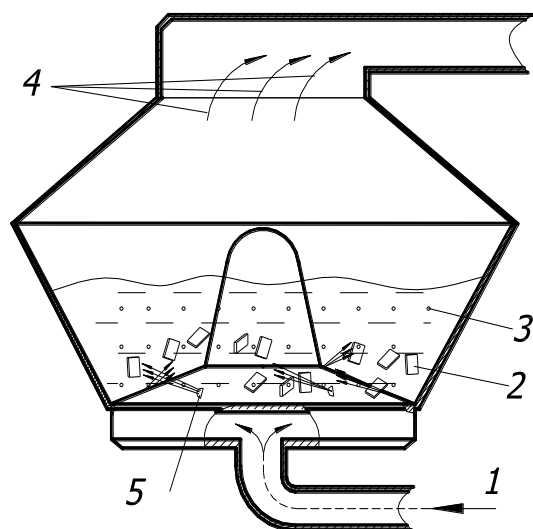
Схема действия струй сжатого воздуха на детали и абразивный материал в жидкости: 1 – сжатый воздух; 2 – обрабатываемая деталь; 3 – абразивное зерно; 4 – отработанный сжатый воздух; 5 – воздушное сопло
